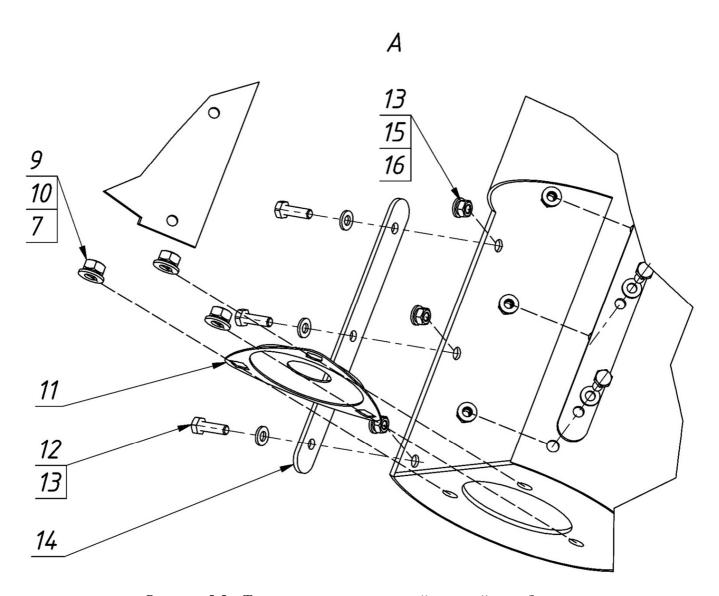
Транспортер разгрузочный верхний в разборе
